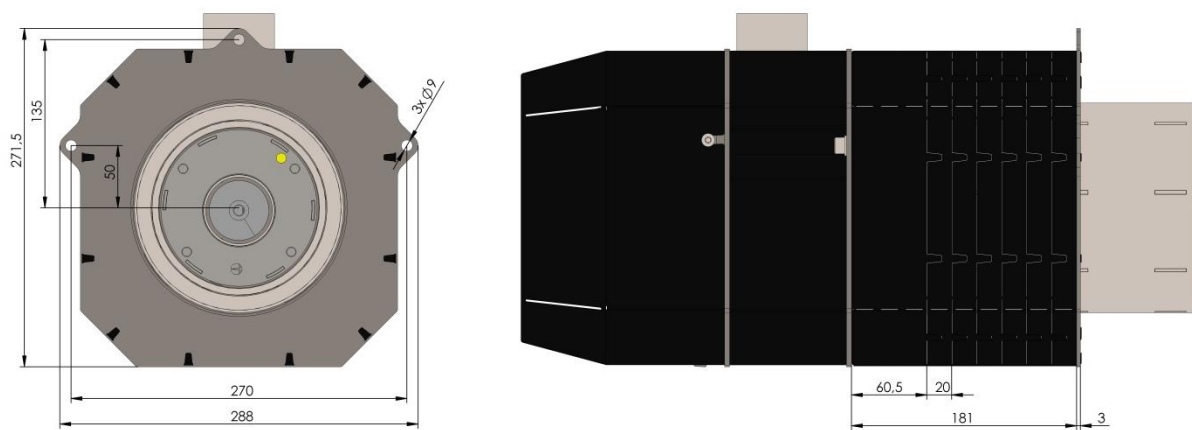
Zobrazení hořáku 8-36 kW s izolačním pláštěm a montážní přírubou
